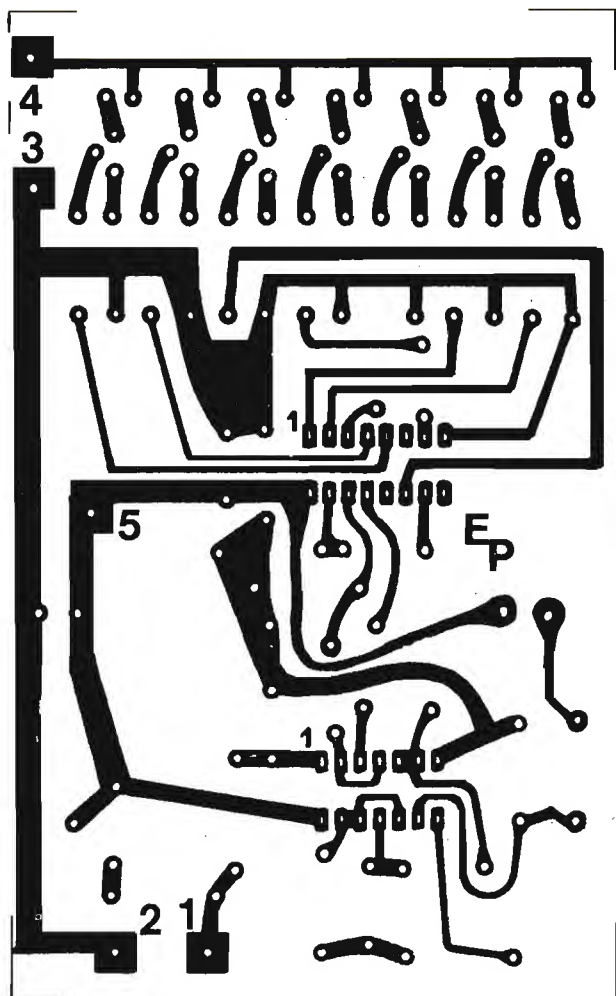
Disegno del circuito stampato che occorrerà riprodurre, nella stessa grandezza, prima di iniziare le operazioni di montaggio del dispositivo.
